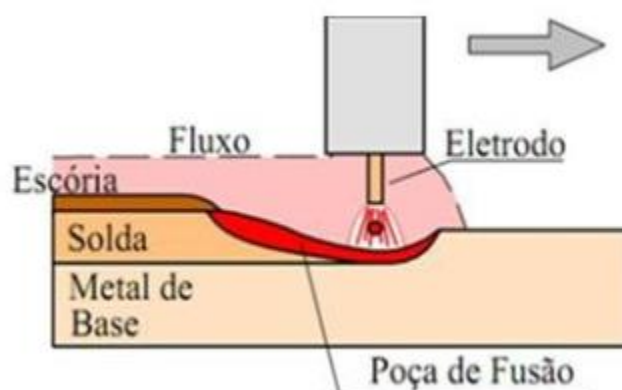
Desenho representativo da soldadura por arco submerso (SAW) [10].
